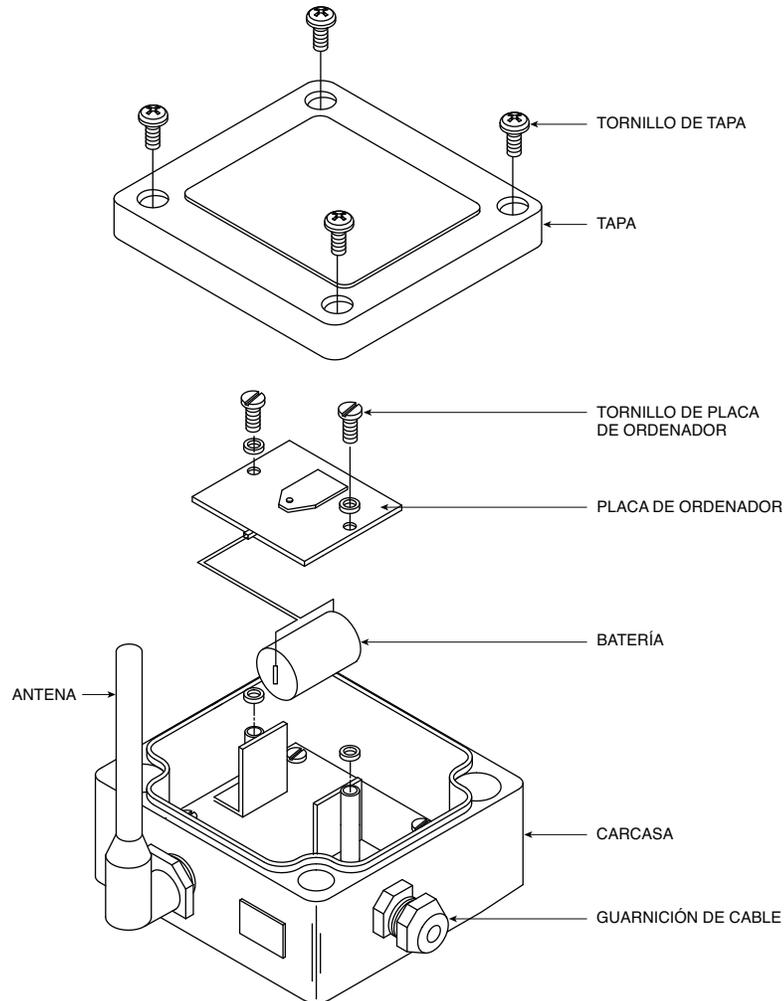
B. Colocación de la batería UWTC-2-NEMA, UWRTD-2-NEMA
